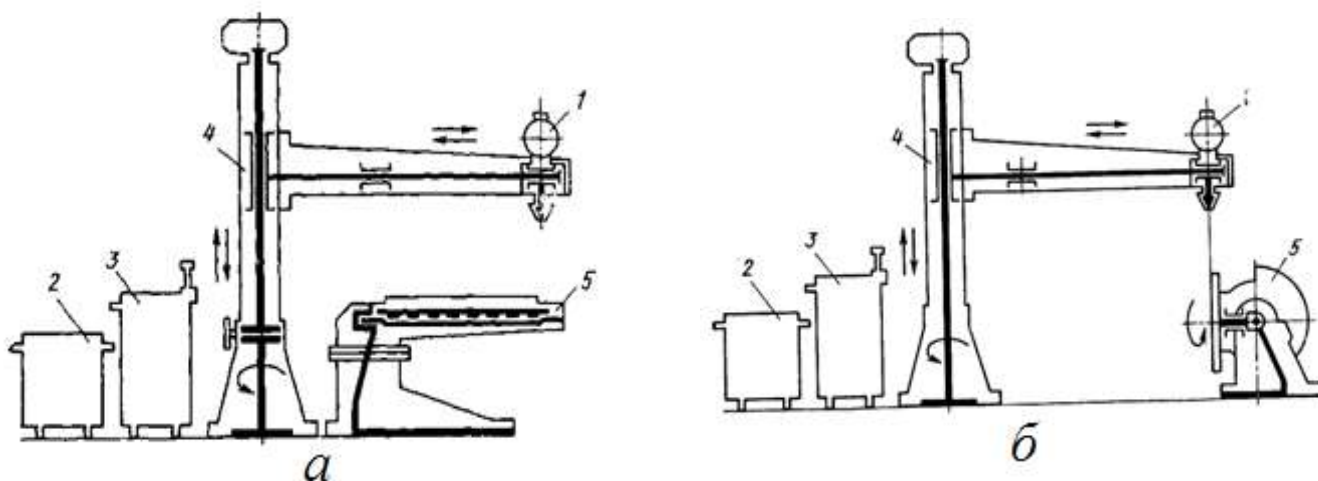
Типові компонування установок для зварювання поздовжніх (а) і кільцевих (б) швів: 1 – зварювальна голівка; 2 – джерело живлення зварювальної дуги; 3 – шафа з електроапаратурою; 4 – поворотна колона для закріплення зварювальної голівки; 5 – пристосування для закріплення виробу
